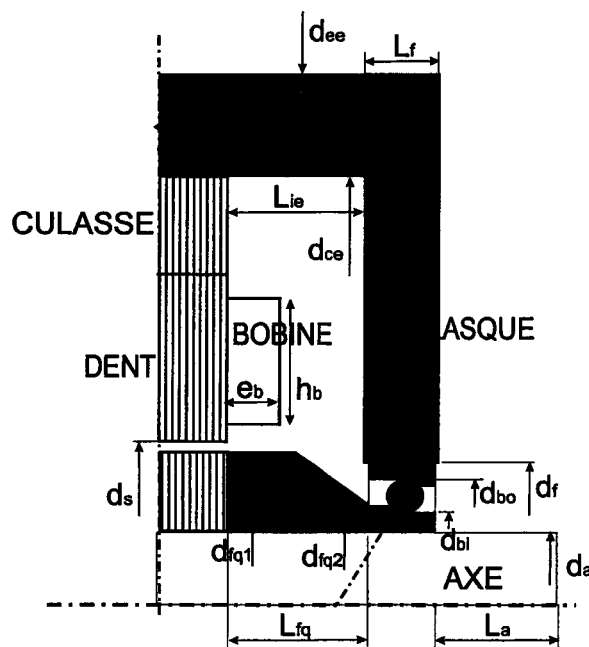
Paramètres dimensionnels du flasque, des roulements et du rotor.
